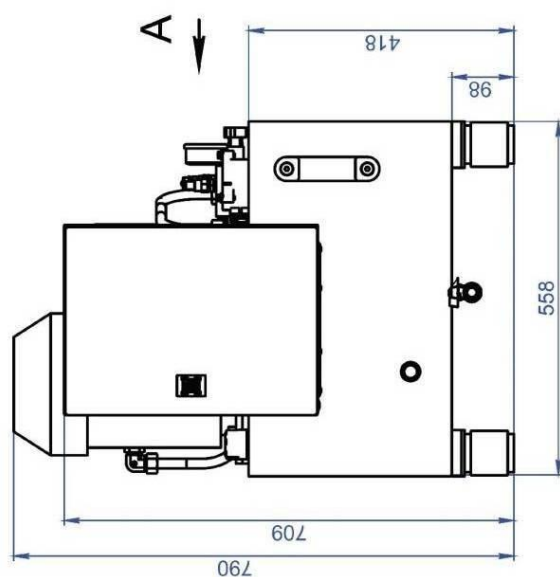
Габаритный чертеж гидравлической станции СГ1-Ш2-1,2/1,2-40-63 МО
